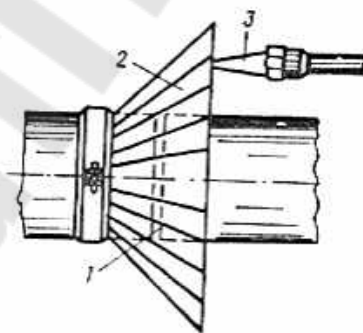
Нагрев стыка сварочной горелкой: 1 - сварочный шов; 2 - стальная или асбестовая воронка; 3 - горелка
